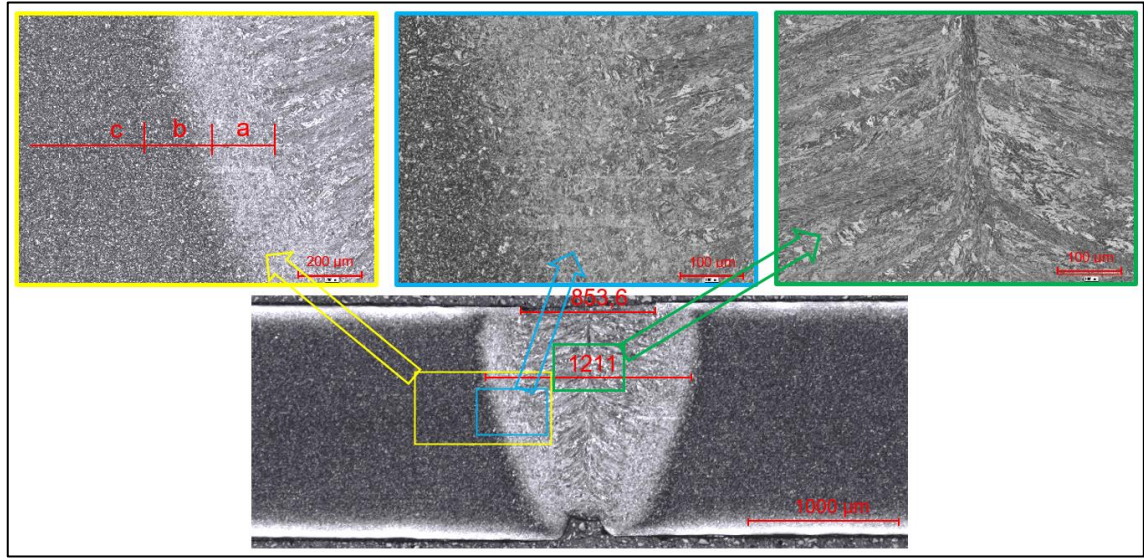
100 mm/sn hızla yapılan birleştirme (Welded sample joined with 100 mm/sec welding speed).
